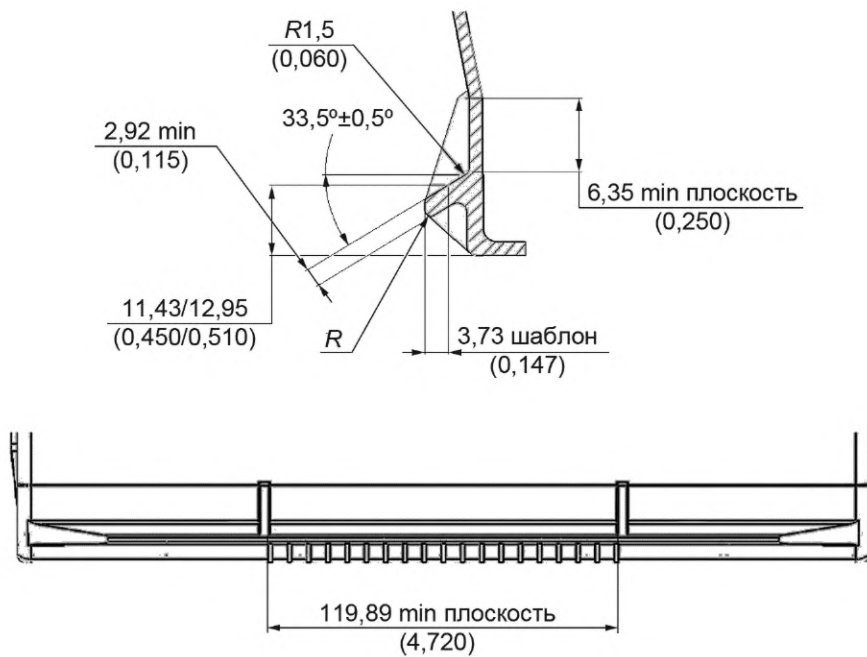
Форма и размеры углублений на корпусе, образующих бортик на короткой стороне корпуса батареи
